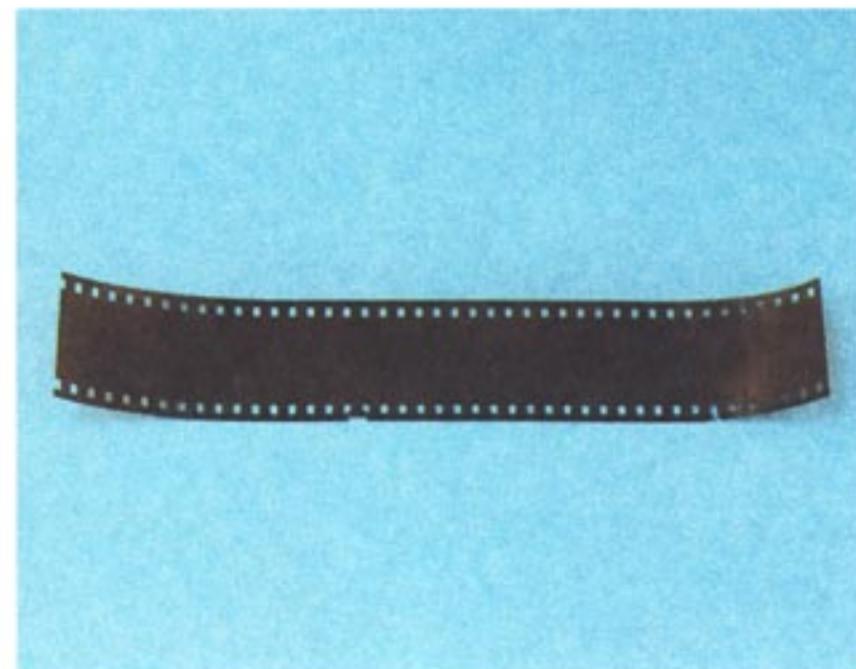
Кусок фотопленки, используемый для разметки заготовки
